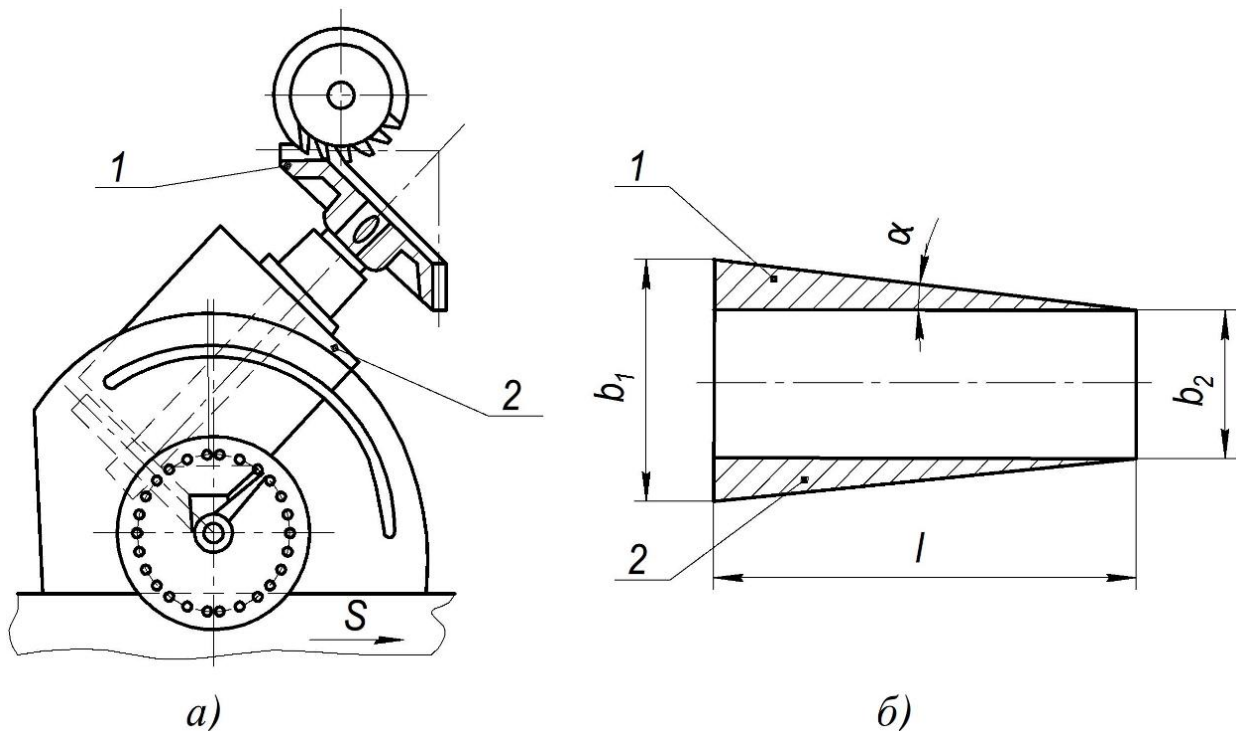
Зубофрезерування конічного зубчастого колеса:
